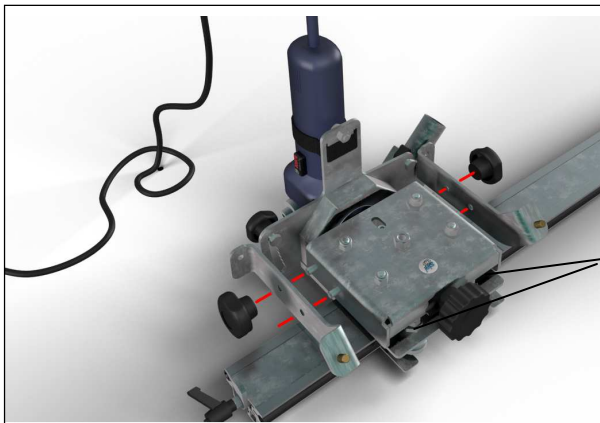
Deux vis de réglage en fonction des dimensions de la meuleuse. Régler la position et serrer les boulons seulement si la meuleuse n'est pas du type Bosch GWS 7-115
